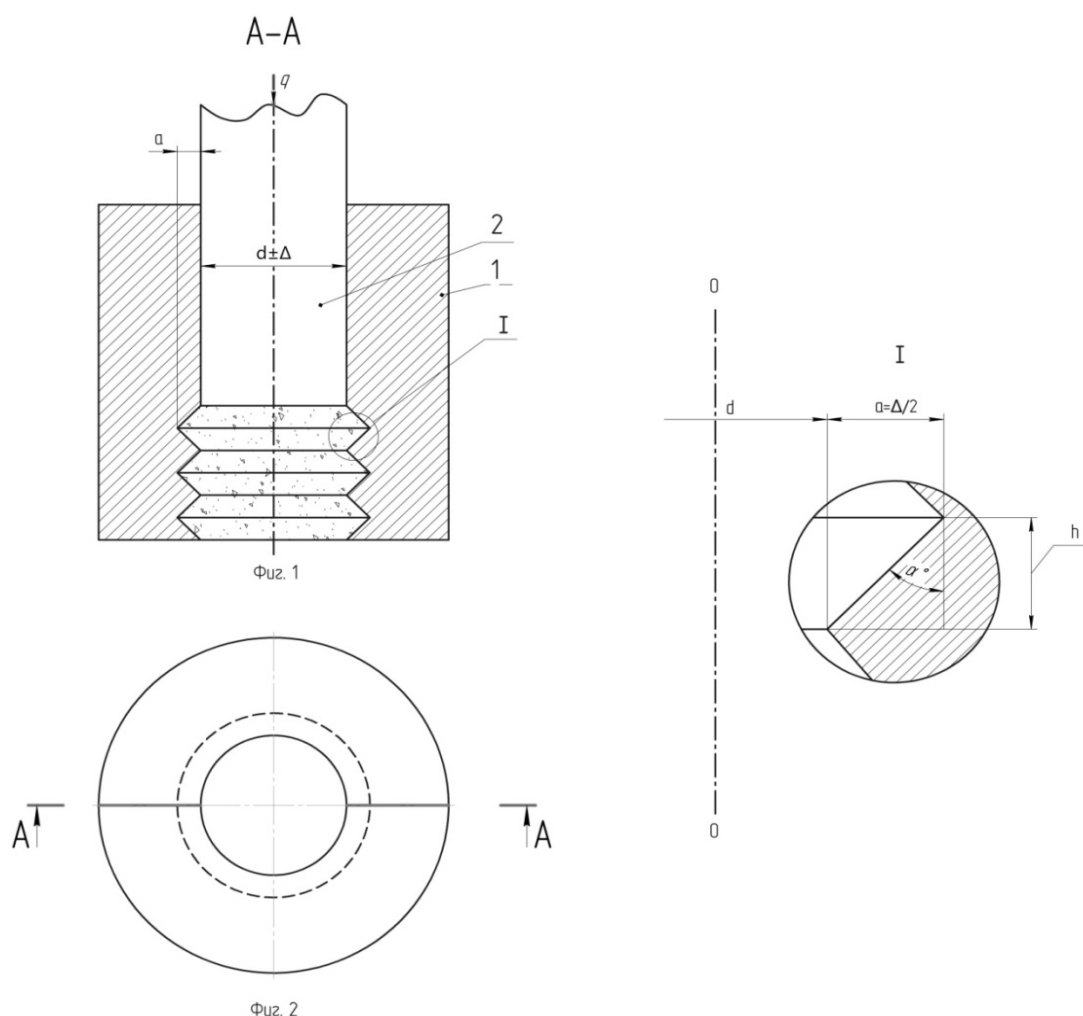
Пресс-форма для прессования порошковых механических увлажненных смесей при изготовлении высокоплотных цилиндрических изделий: 1 – матрица, 2 – пуансон
